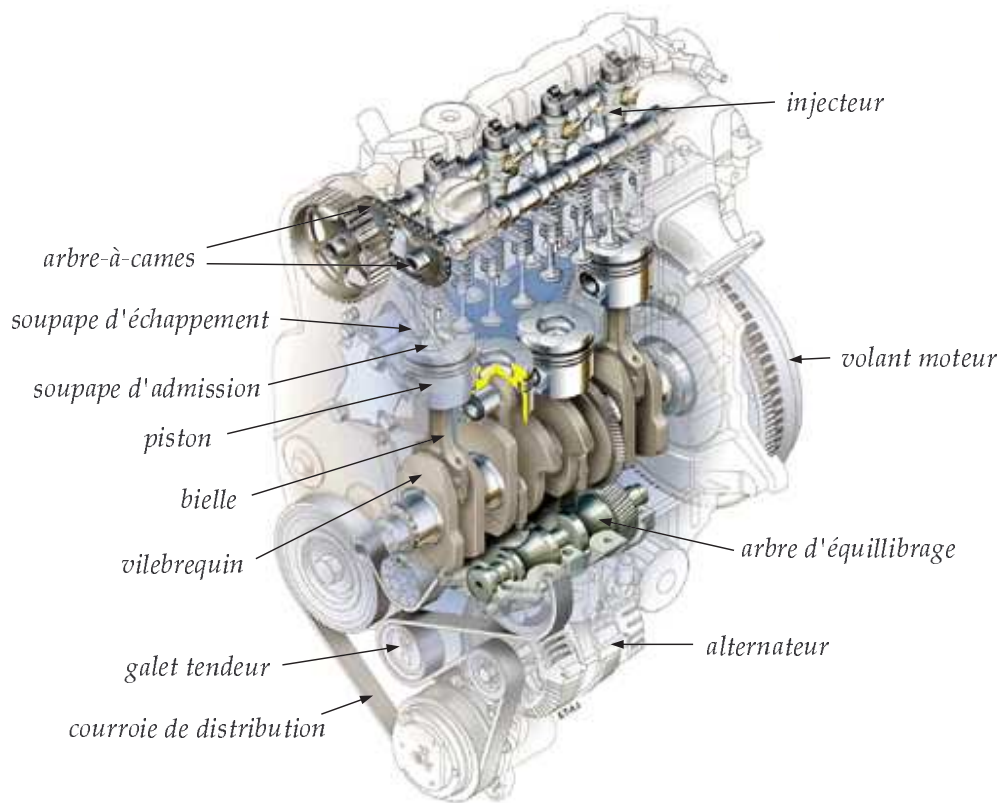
Vue d'ensemble d'un moteur (source image : [3])
